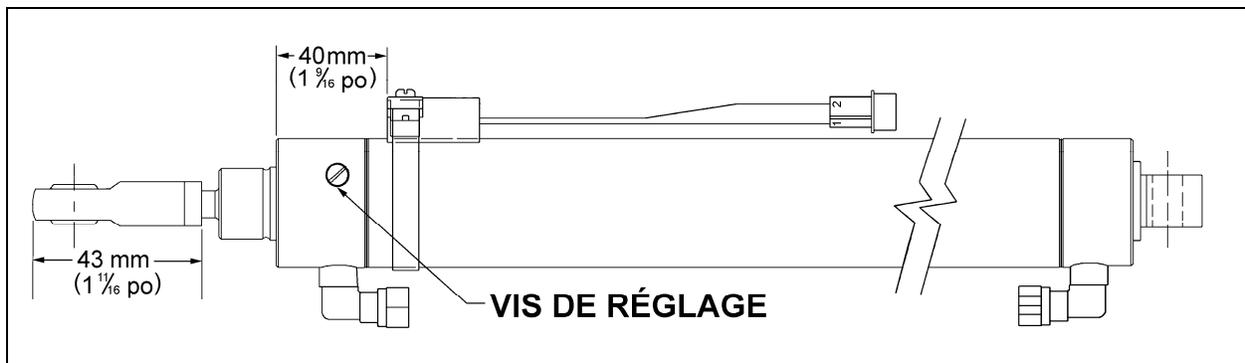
ENSEMBLE DU CYLINDRE PNEUMATIQUE DE 2 POUCHES
